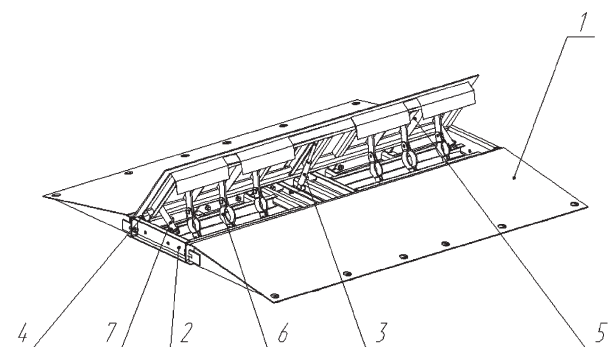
Типовая конструкция дорожного блокиратора с подъемной платформой: 1 — пандус; 2 — рама; 3 — гидравлический привод; 4 — шарнирное соединение; 5 — подъемная платформа; 6 — рычаги; 7 — механизм фиксации
